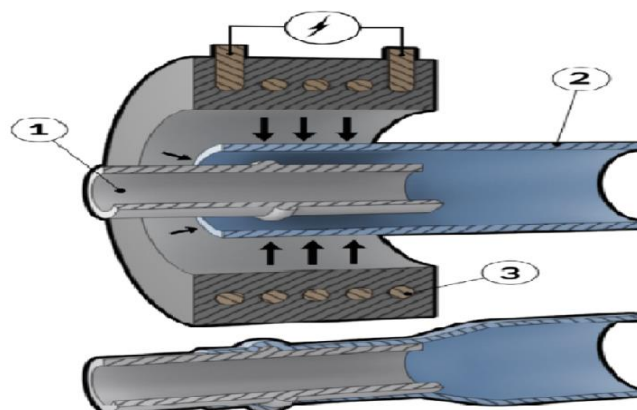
Soudage de tubes (1) Pièce intérieure, (2) Pièce extérieure, (3) L'inducteur[5]
